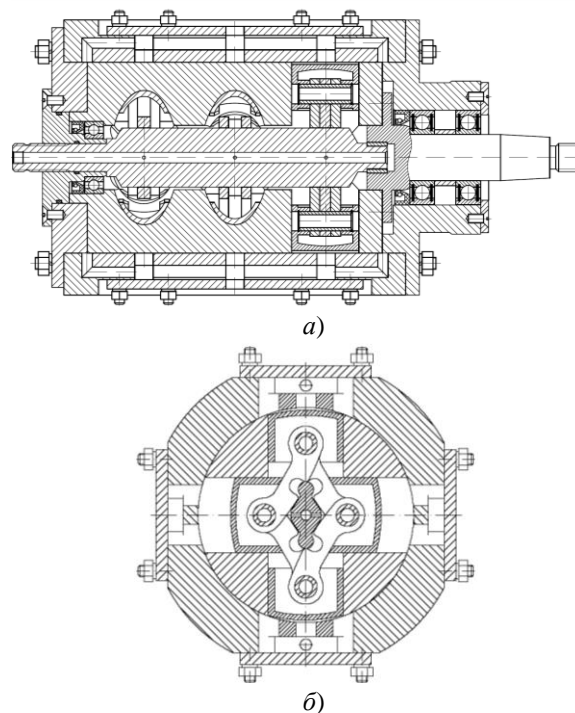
Роторно-поршневий пневмодвигун РПД-4,4/1,75: а – поздовжній розріз; б – поперечний розріз
